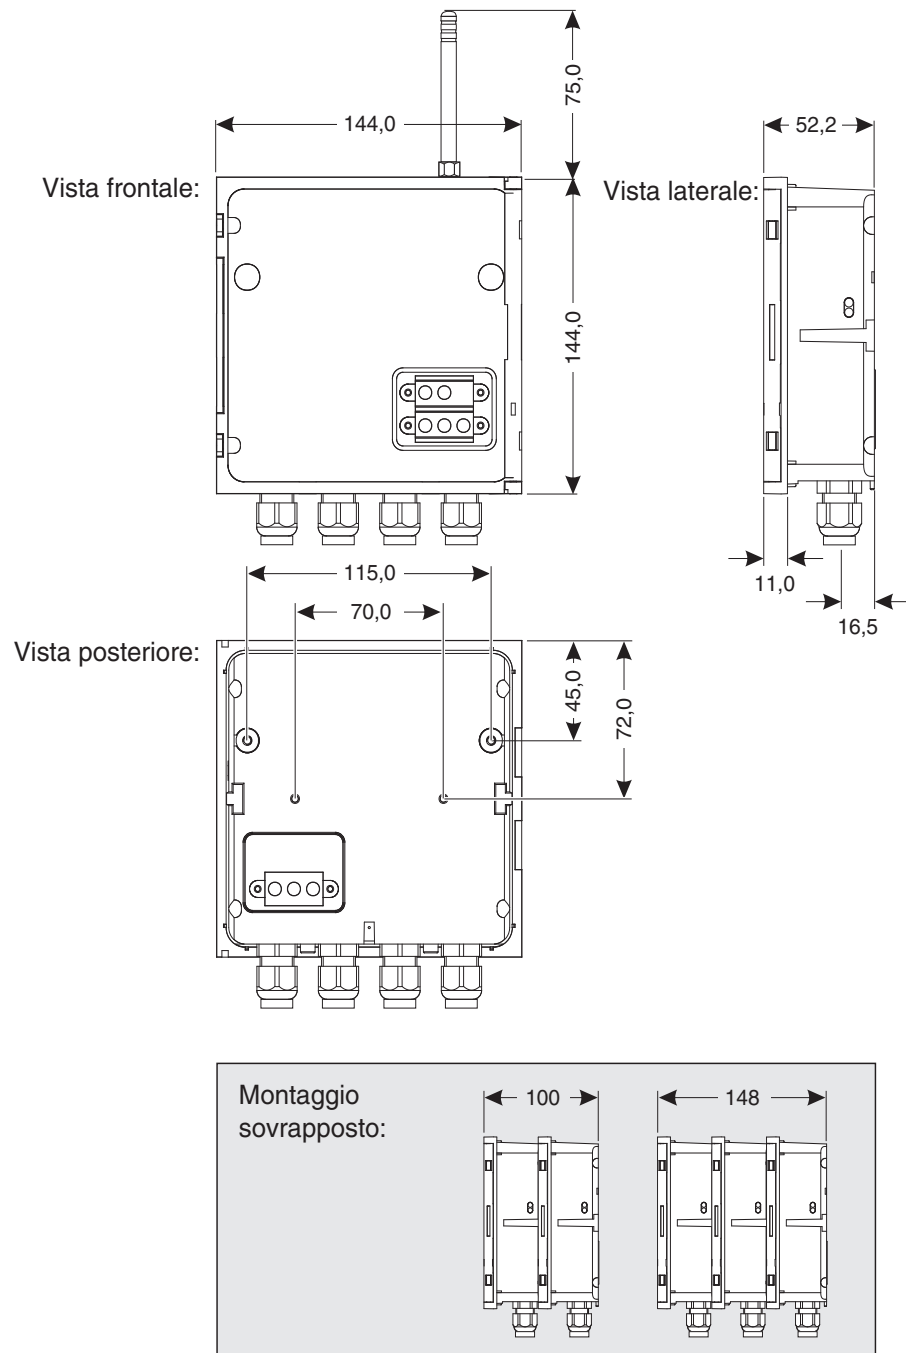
Disegno dimensionale per modulo MIQ (dimensioni in mm)
